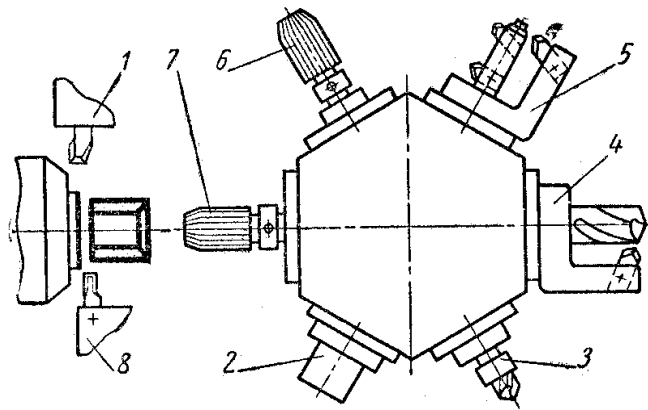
Схема обробки втулок із прутка на токарно-револьверному верстаті: 1 – підрізка торця; 2 – подача прутка до упору; 3 – зацентрування під свердлування; 4 – свердлування отвору та обточування зовнішньої поверхні; 5 – розточування отвору, зняття фасок; 6 – попереднє розгортання; 7 – остаточне розгортання; 8 – відрізка.
